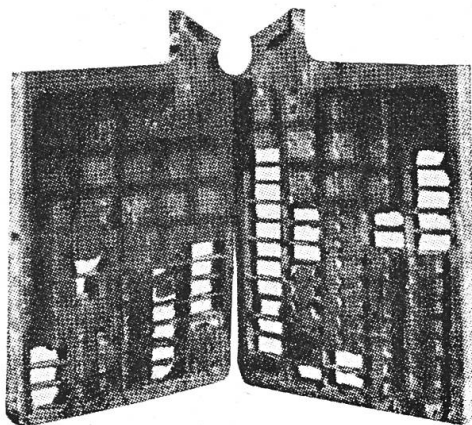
Par suite de trépidations (mauvaise fixation) la masse active est sortie des grilles de plaques.
